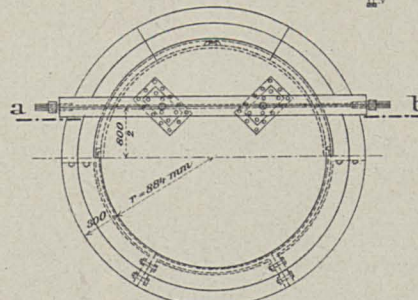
Grundriss des Deckels und des Ventil-sitzes. 1: 60.
